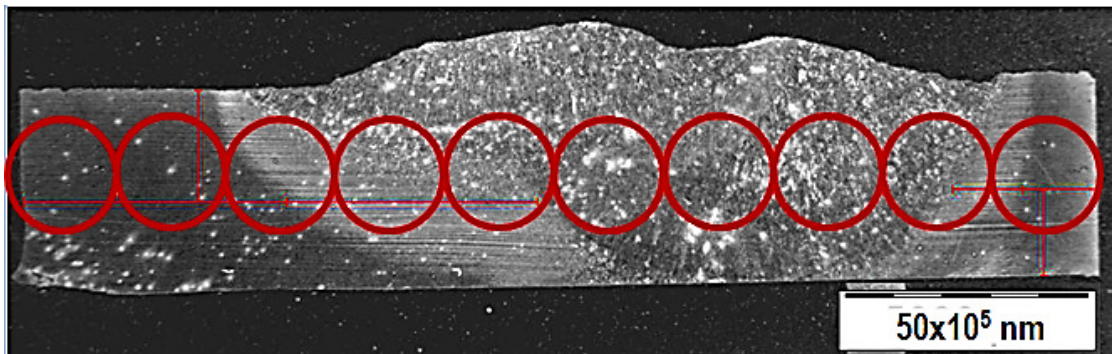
Representación de barrido de soldadura mediante UT.
